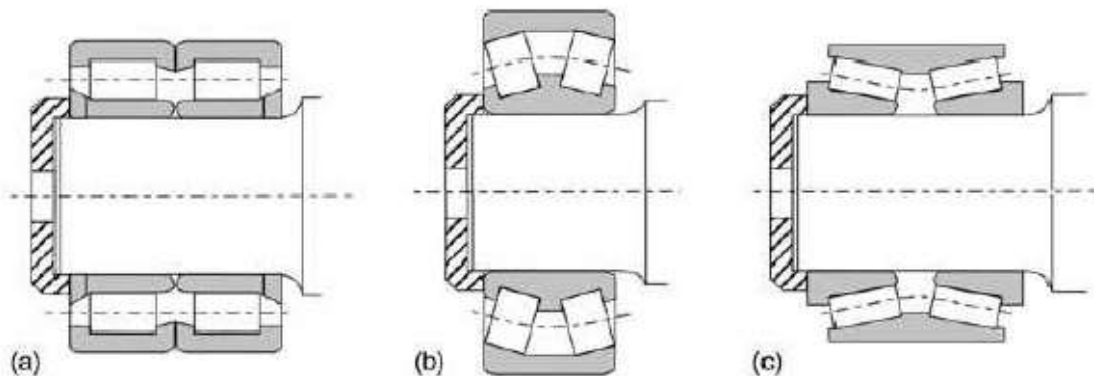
Diseños de rodamientos de rodillos (a) Cilíndrico de dos hileras, (b) Autoalineado de una hilera, (c) Cónico de dos hileras[3].
